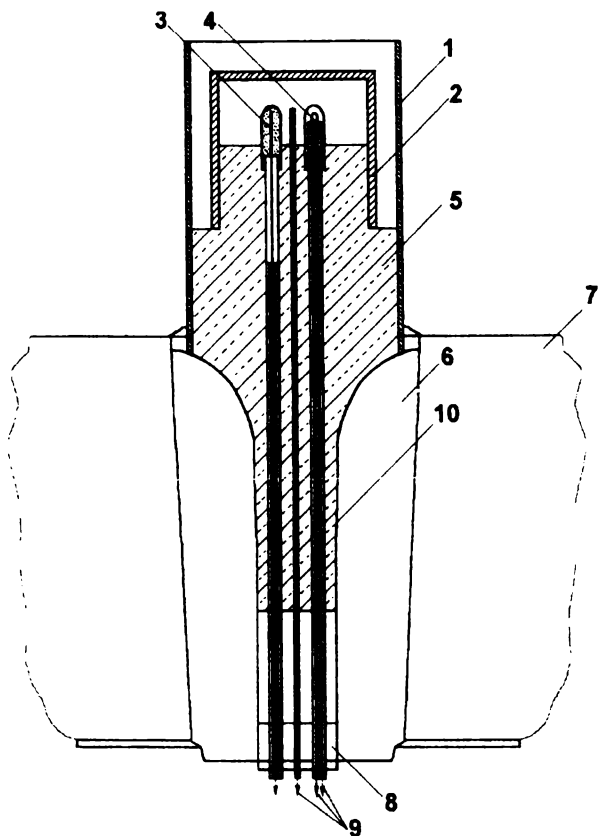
Устройство для замера окисленности и температуры металла в ковше: 1, 2 – металлическая защита; 3, 4 – датчики окисленности и температуры; 5 – огнеупорный блок; 6 – сталеразливочный стакан; 7 – футеровка ковша; 8 – металлическая пробка; 9 – токоотводы; 10 – огнеупорная обмазка
